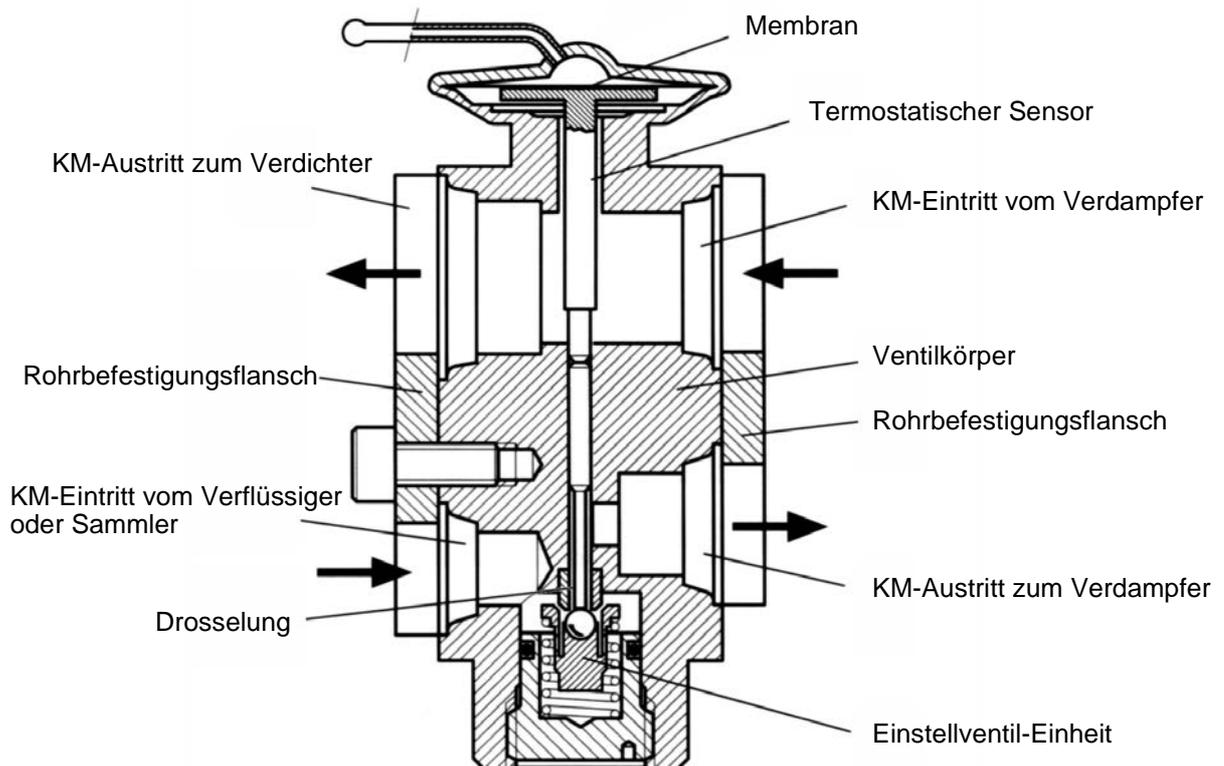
TEV mit äußerem Druckausgleich (Blockventil)
